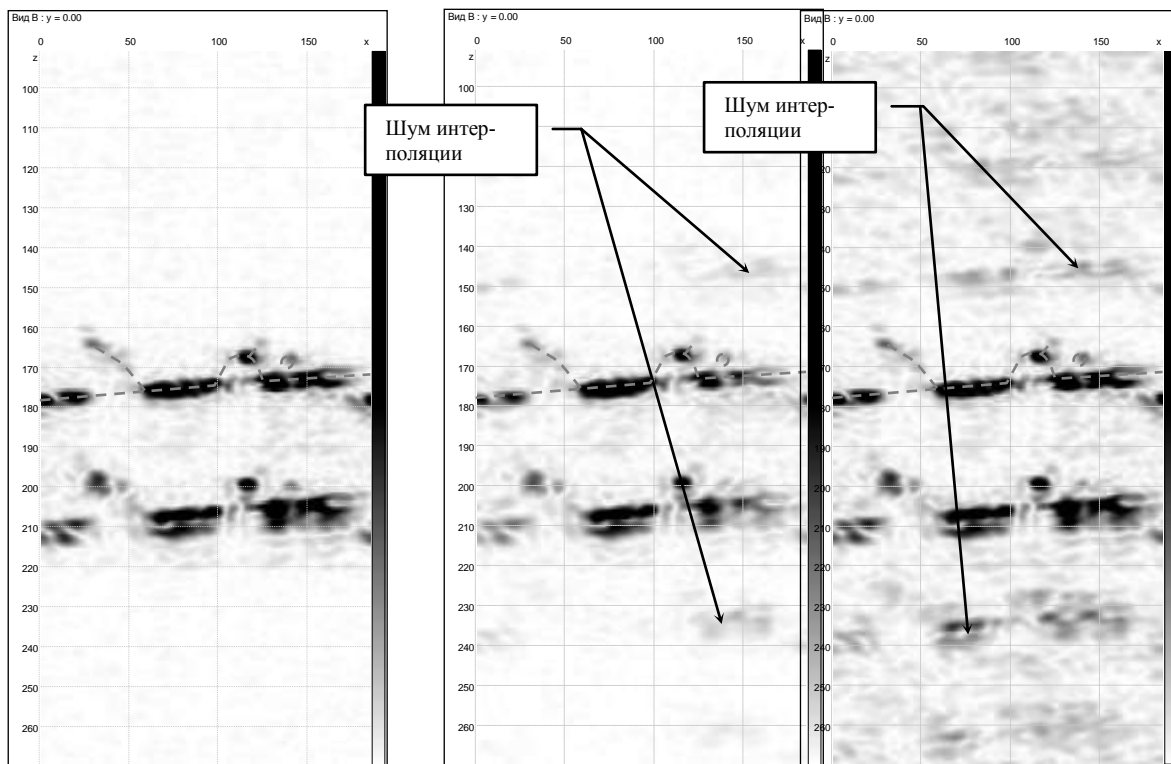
Результат восстановления изображений образца сварного соединения. Серыми пунктирными линиями показаны границы шва, естественный и искусственный дефекты.
